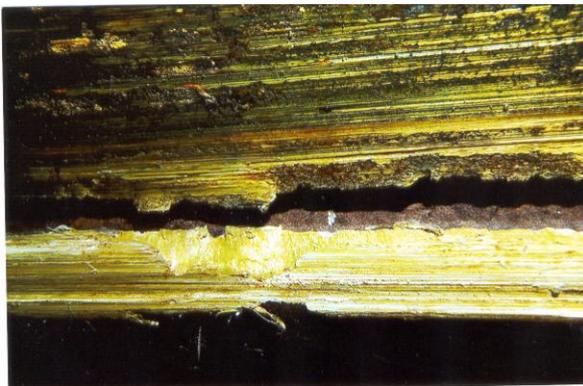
Grieta de 8.300 x 30 mm
